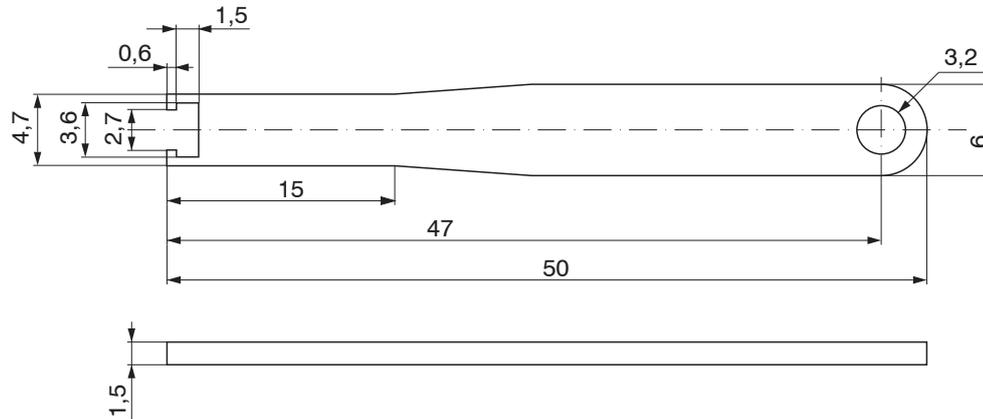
MML Extraction Tool H2.5 & H2.0, Artikel R302309000
